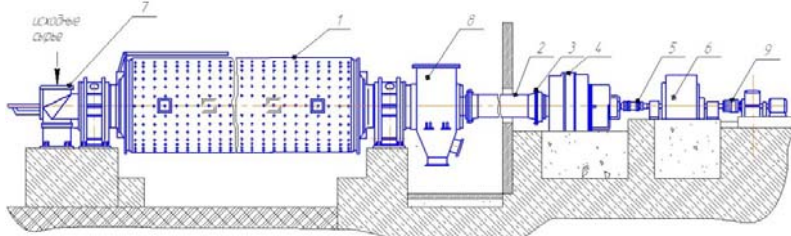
Общий вид мельницы: 1 - барабан; 2 - провал; 3 - зубчатая муфта; 4 - планетарный редуктор; 5 - зубчатые муфты; 6 - приводной электродвигатель; 7 - устройство загрузки сырья; 8 - устройство выгрузки продукта; 9 - вспомогательный привод
